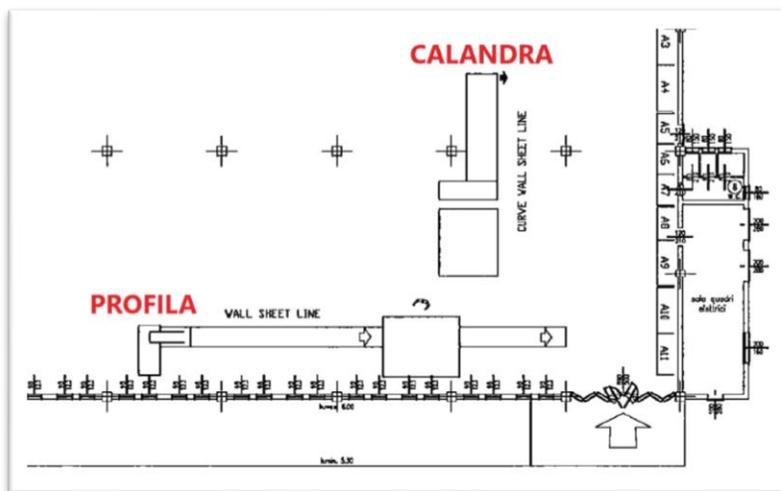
layout delle fasi produttive delle lamiere
